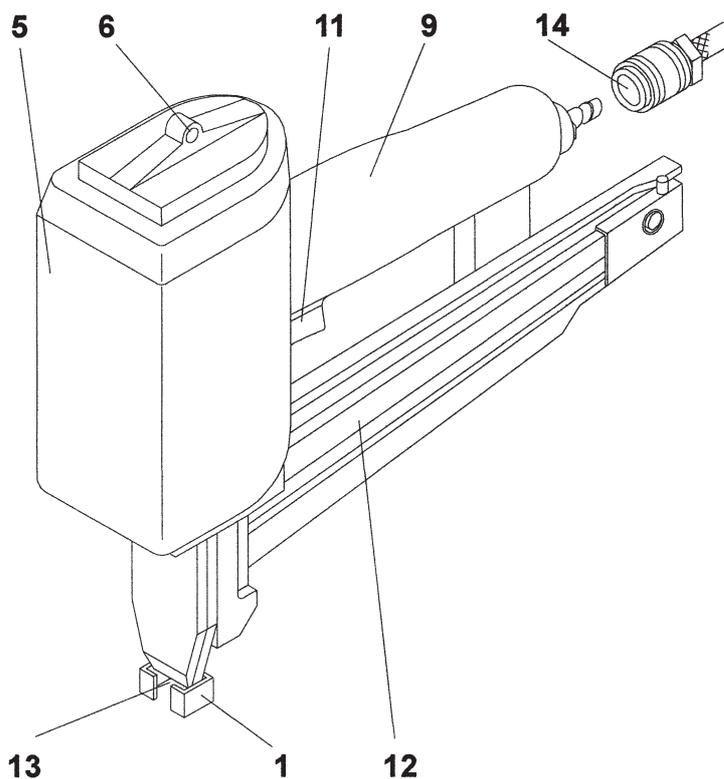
Beispiel einer Gesamtansicht eines druckluftbetriebenen Eintreibgerätes
